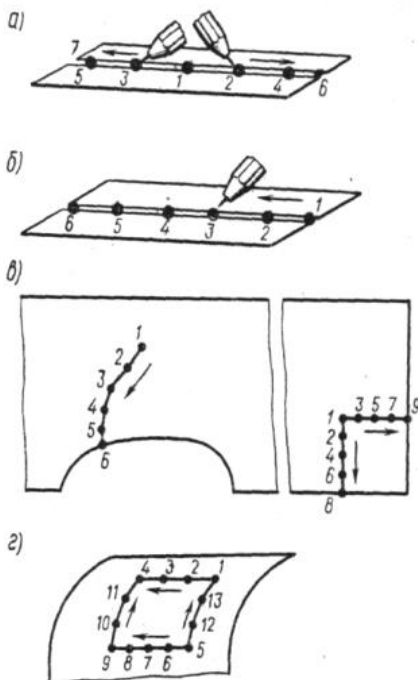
Последовательность расположения точек сварки: а - наложение прямолинейного шва; б - прихватка точками при формировании угла; в - прихватка трещин; г - сварка точками замкнутого шва
